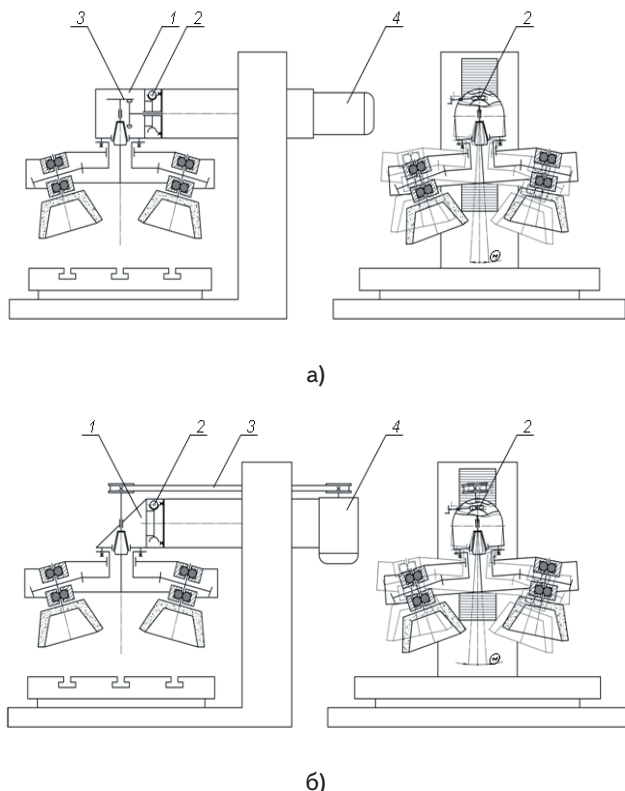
Схема установки ТПШГ на плоскошлифовальный станок
